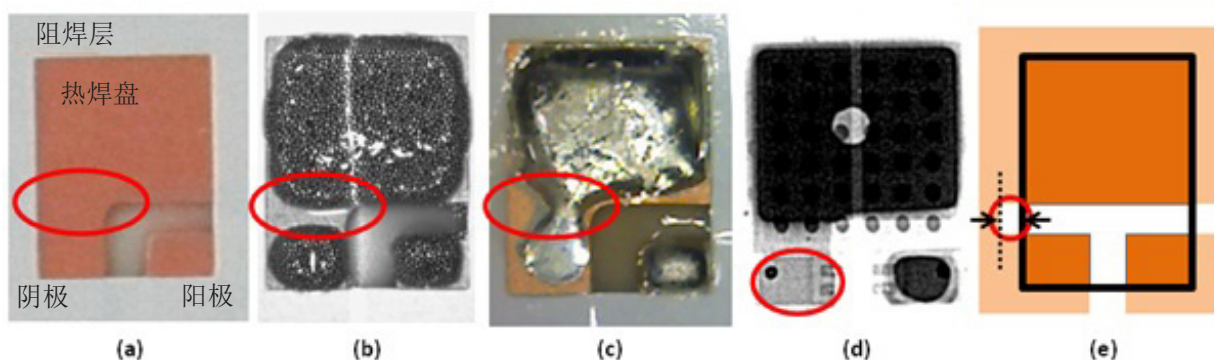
不正确的PCB版图设计可能会导致焊膏从小尺寸电极焊盘移至邻近更大的热焊盘。在这个案例中，负极无需任何阻焊缓冲层就能直接地连接到热焊盘之上（a）。尽管热焊盘和负极上的锡膏在涂覆不久以后并不连贯（b），然而回流后锡膏能将负极焊盘与热焊盘粘连在一起（c）。在最坏的情况下，锡膏从小尺寸负极焊盘移至大尺寸热焊盘上会导致器件开路（d）。因此在设计PCB时，即便阻焊层与金属层在对准时可能发生最差的情况，热焊盘与电极焊盘之间的任何连接都要用阻焊层覆盖（e）。
